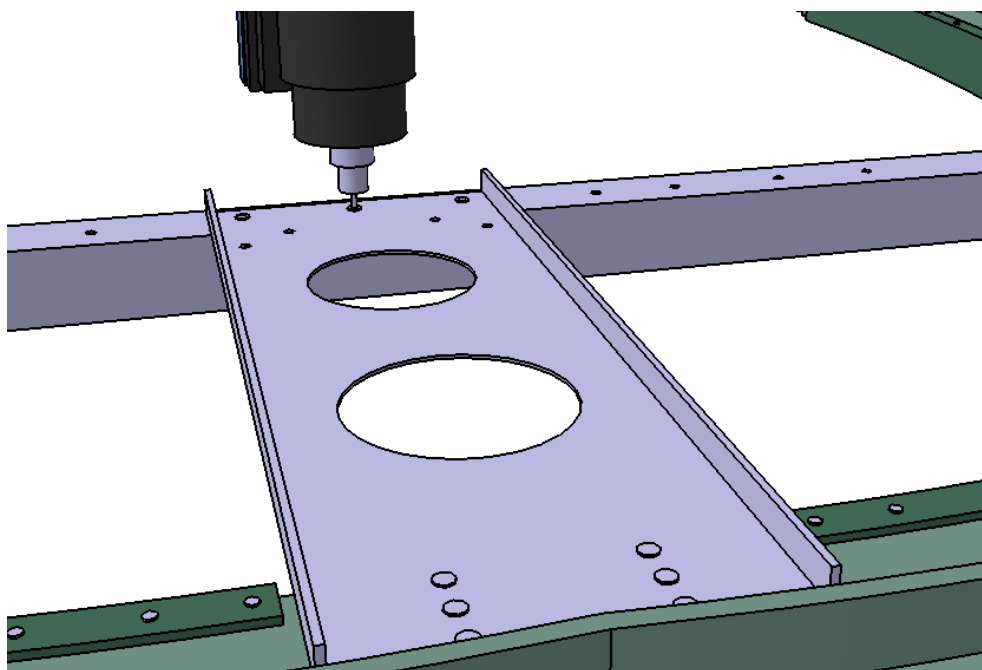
Cuaderna 9: Remachado refuerzo central
